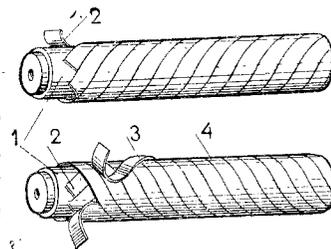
Технология изготовления цилиндрического корпуса типа «монокок» из ленты бумаги или из деревянной стружки:
